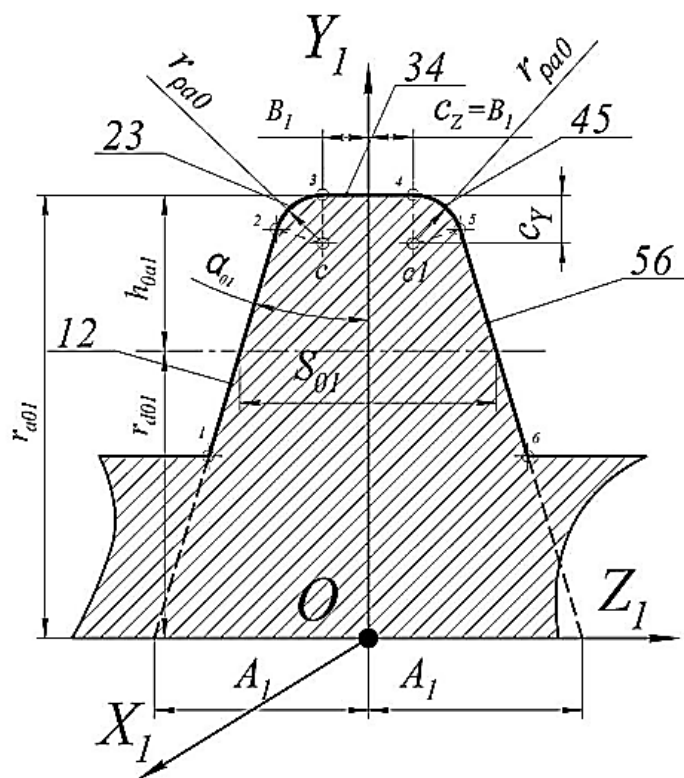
Твірний профіль вихідної інструментальної поверхні стандартної черв’ячної фрези
